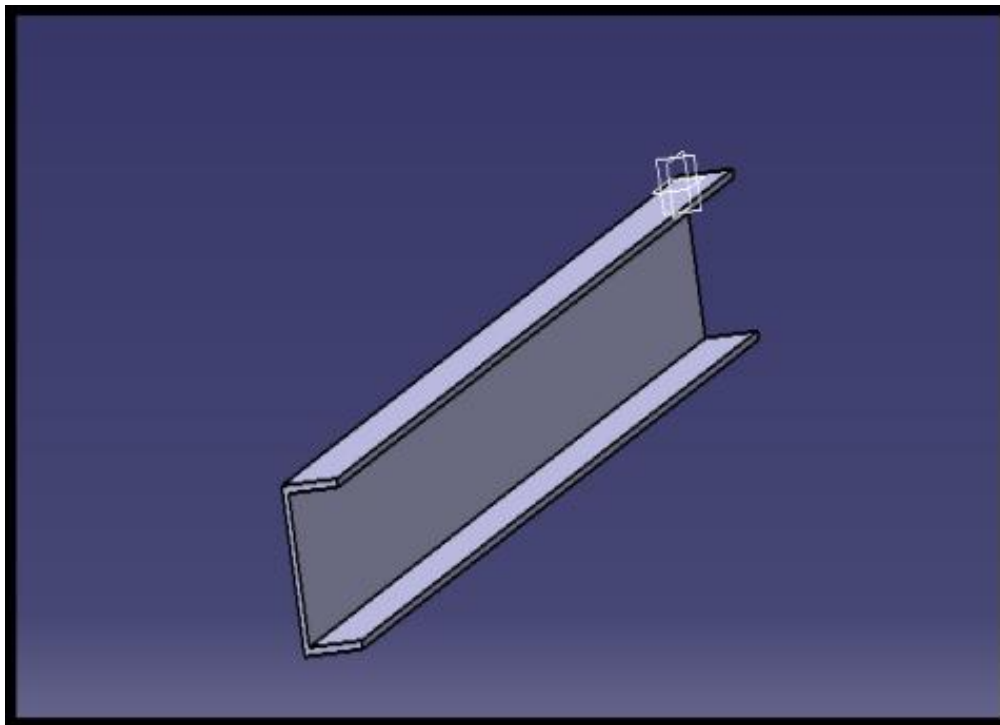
Modelagem tridimensional do perfil estrutural em seção "C" (C-Section/Channel)
